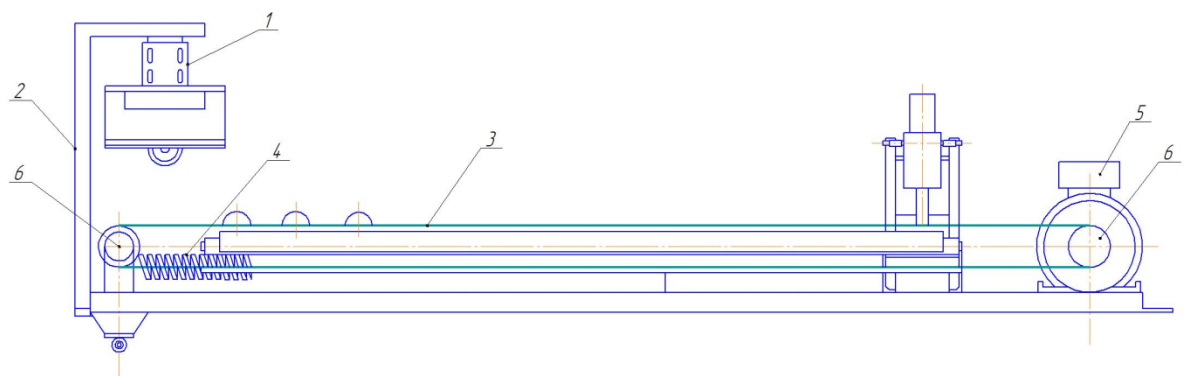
Общий вид посадчика Г4-ПТЗ: 1— питатель; 2 – рама; 3 – лента; 4 –пружина; 5 – привод; 6 – вал.
